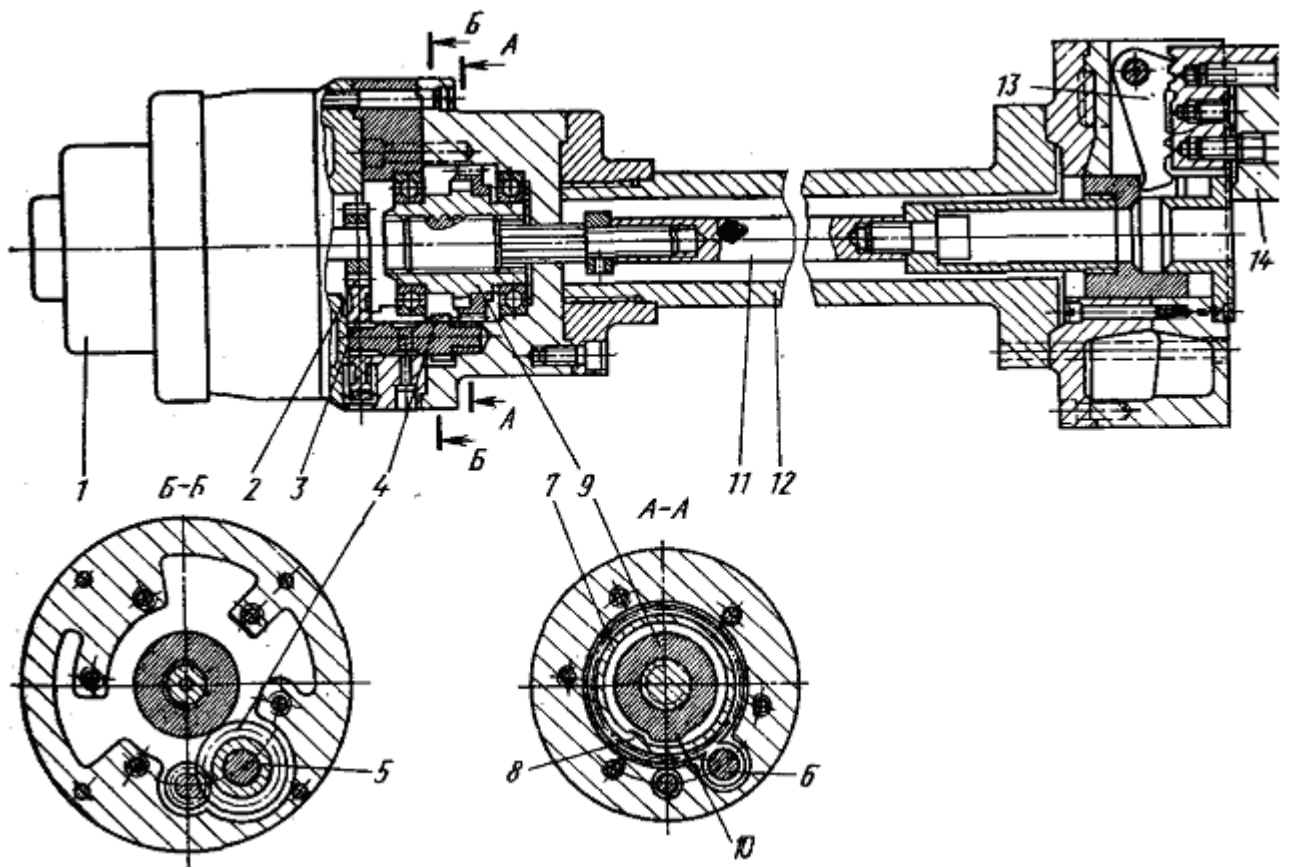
Электромеханический привод рычажного токарного патрона
